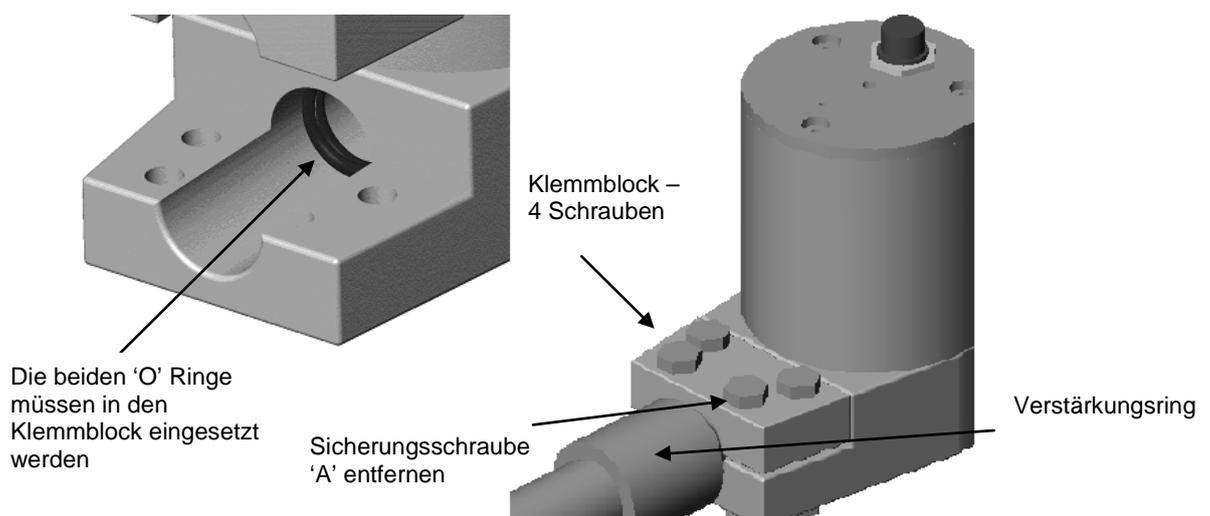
Montage von Sensorarm und Sensorgehäuse
